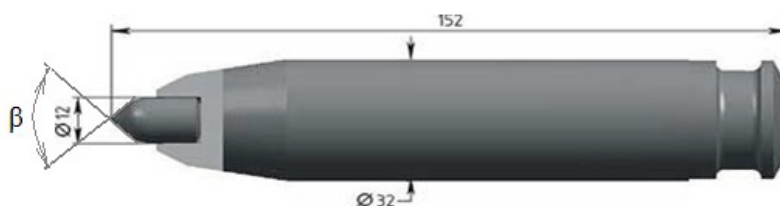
Общий вид поворотного резца РКС – 1
